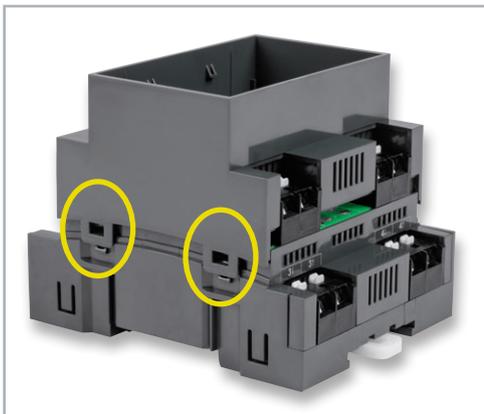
So wird das Gehäusemittelteil aufgesetzt ...
